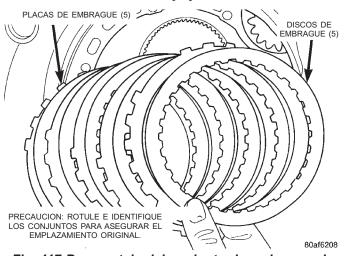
Desmontaje del conjunto de embrague de baja y marcha atrás
